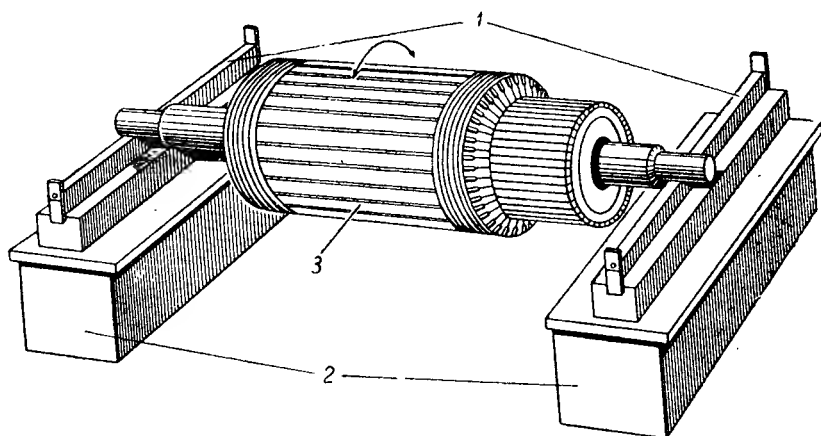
Параллели для статической балансировки коллекторов и якорей
